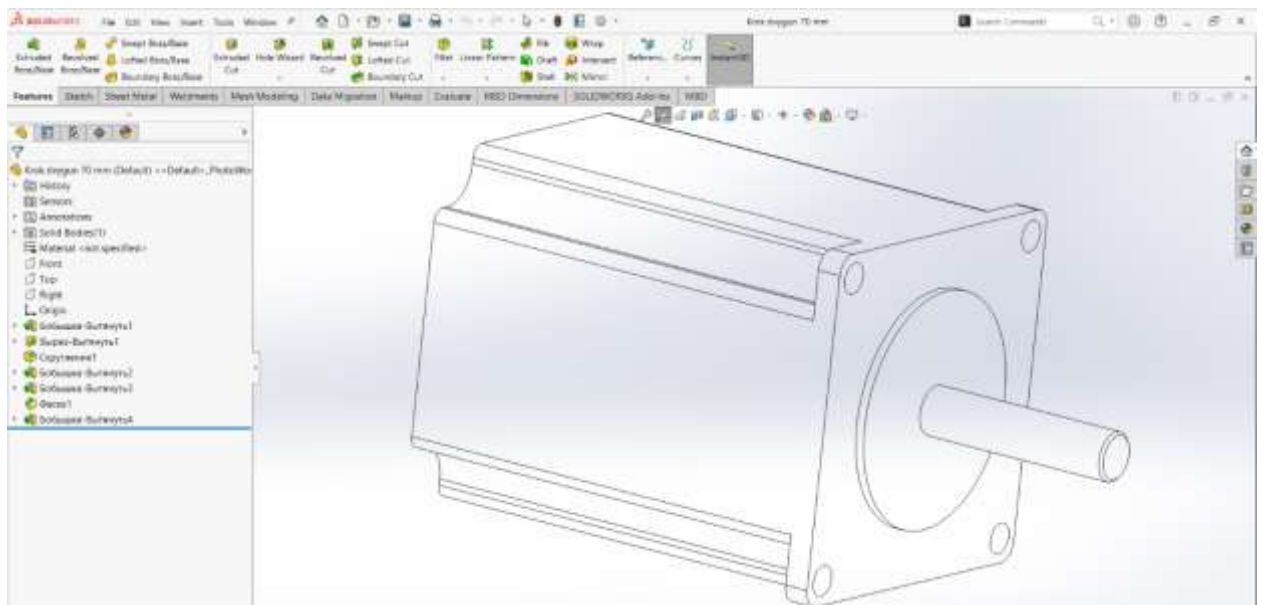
Змодельований кроковий мотор поворотного столу
